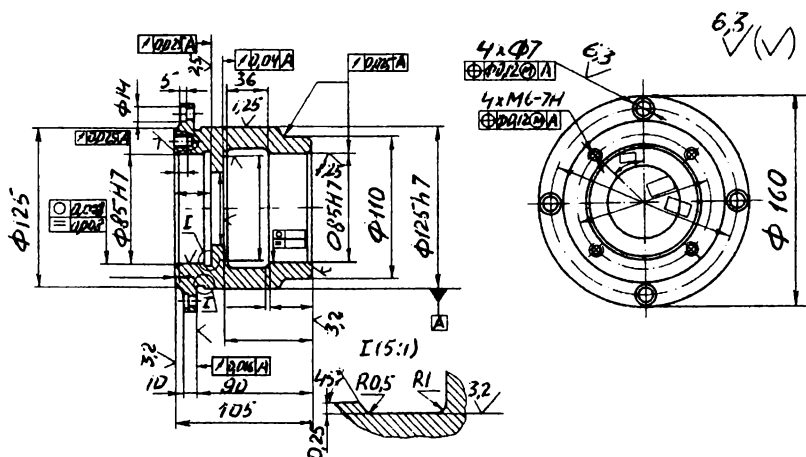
Пример оформления чертежа детали "Втулка"
